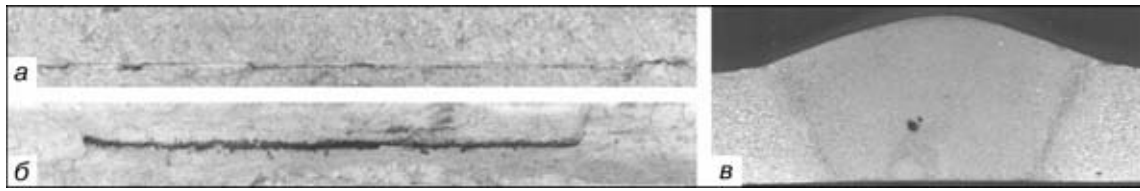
Протяженные нитевидные включения оксидной пленки в изломах швов (а, б) и на поперечном макрошлифе (в), образующиеся при аргонодуговой сварке литийсодержащих алюминиевых сплавов неплавящимся электродом
